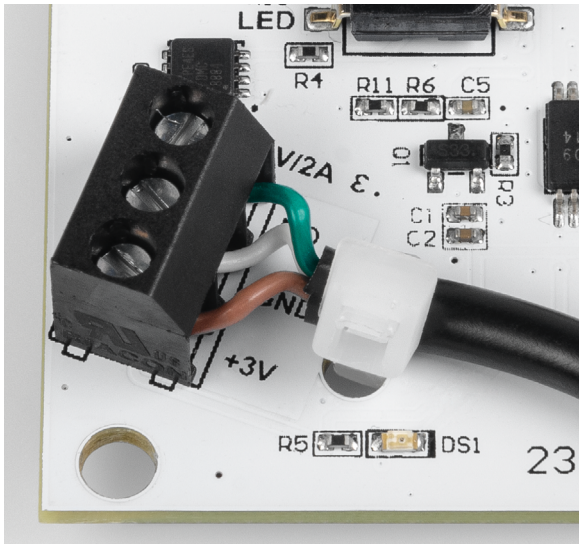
Fixierung der Zuleitung mit einem Kabelbinder
